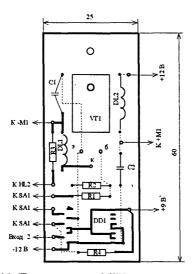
Печатная плата УПТ двигателя редуктора
